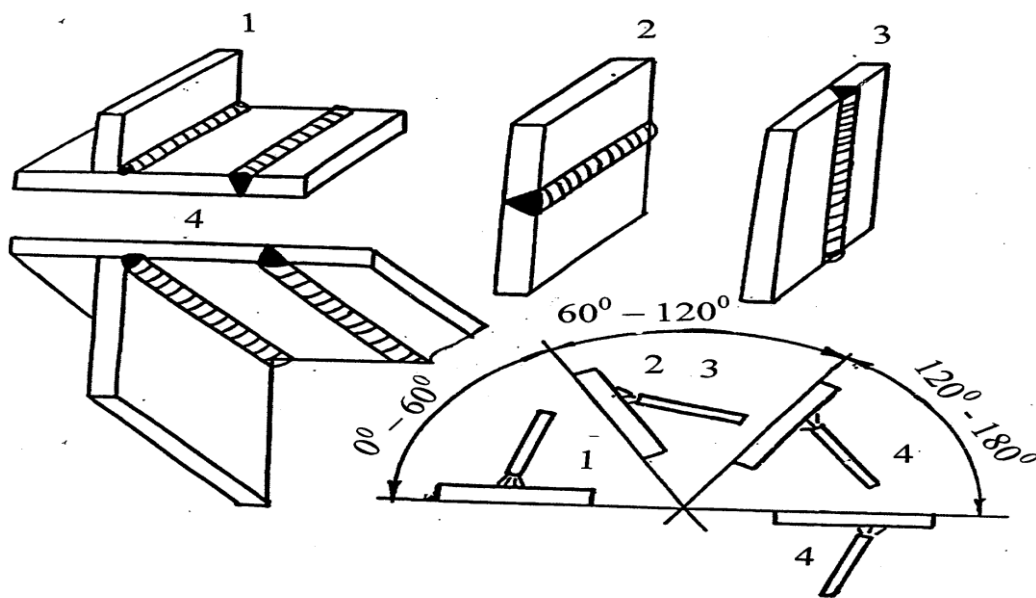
Положение сварных швов в пространстве:
